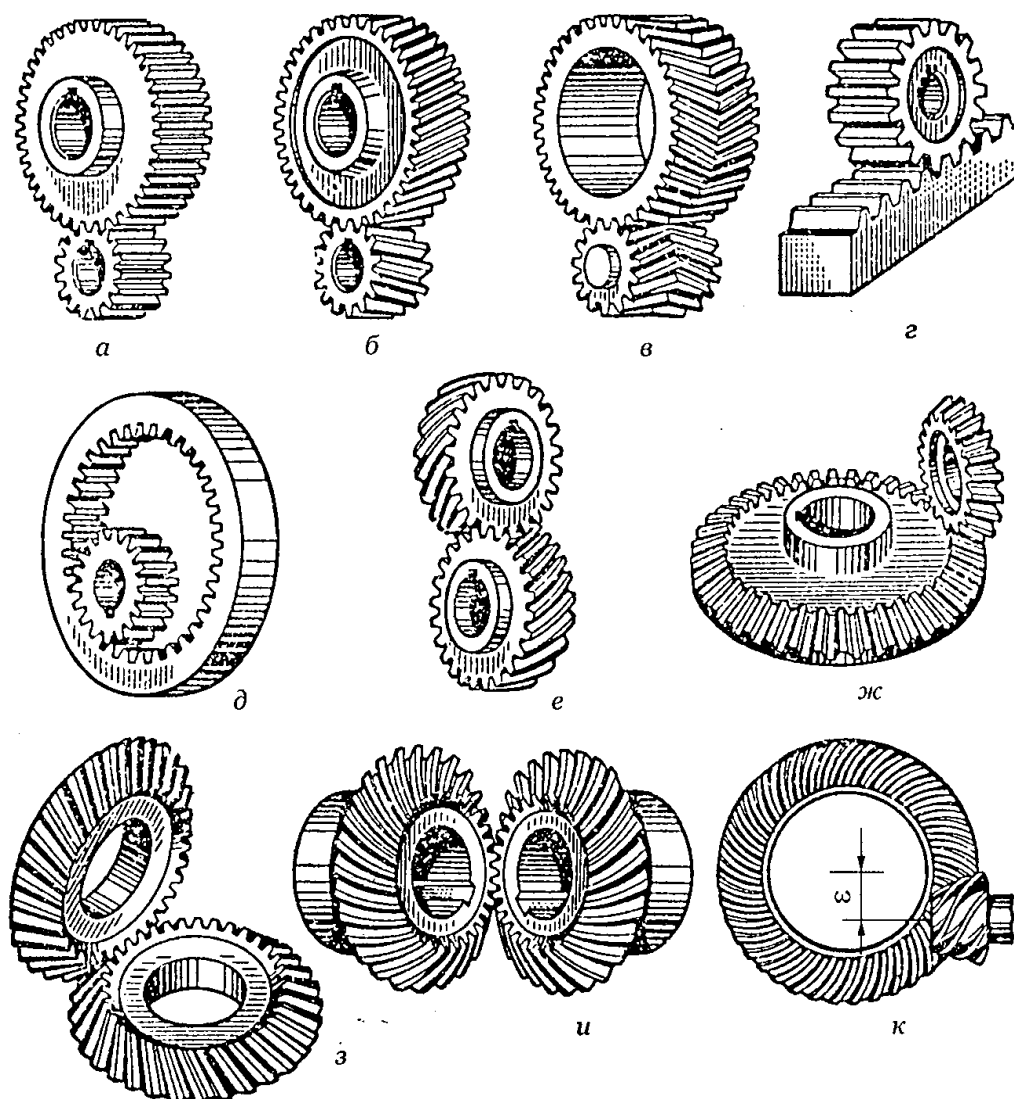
Типы зубчатых передач: цилиндрические с внешним зацеплением (а — с прямозубыми колесами; б — с косозубыми колесами; в — с шевронными колесами); г — шестерня — рейка; д — цилиндрические с прямыми зубьями и внутренним зацеплением; е — цилиндрическая винтовая; конические передачи (ж — с коническими прямозубыми колесами; з — с коническими косозубыми колесами; и — с круговыми зубьями; к — гипоидная передача со скрещивающимися валами); е — расстояние между осями валов
